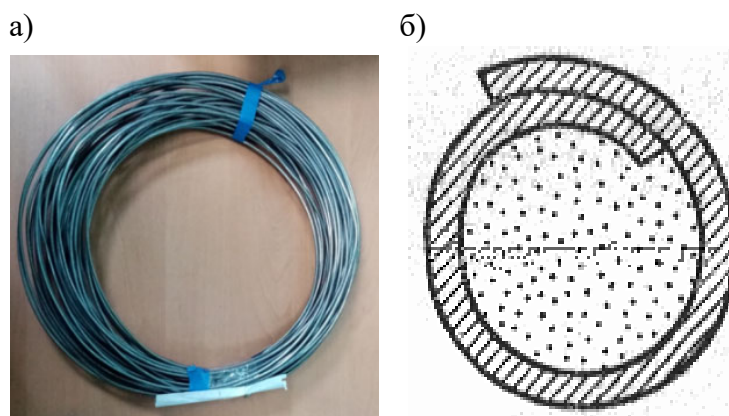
Полученная сварочная проволока (а) и вид её сечения (б)
